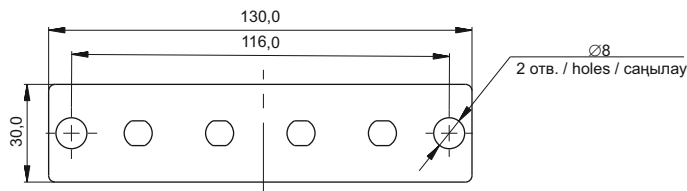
Габаритные и установочные размеры панели FOBX-P04-FC-R / Figure 6 – Overall and mounting dimensions of the panel FOBX-P04-FC-R / 6 сурет – FOBX-P04-FC-R панелінің габариттік
